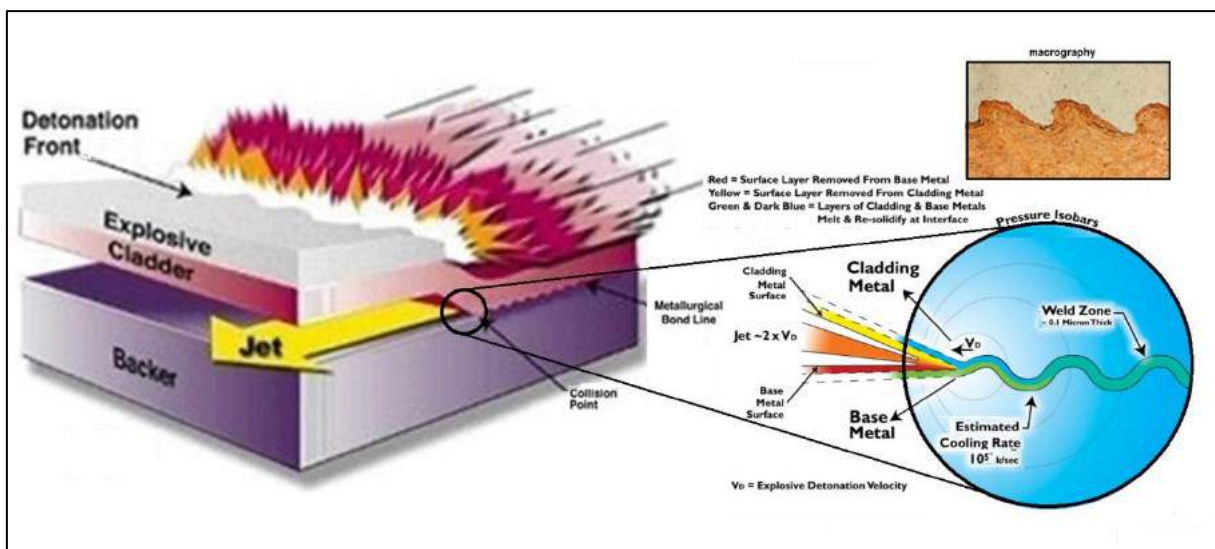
Revestimento soldados por explosão (Pauly, 2012.)
